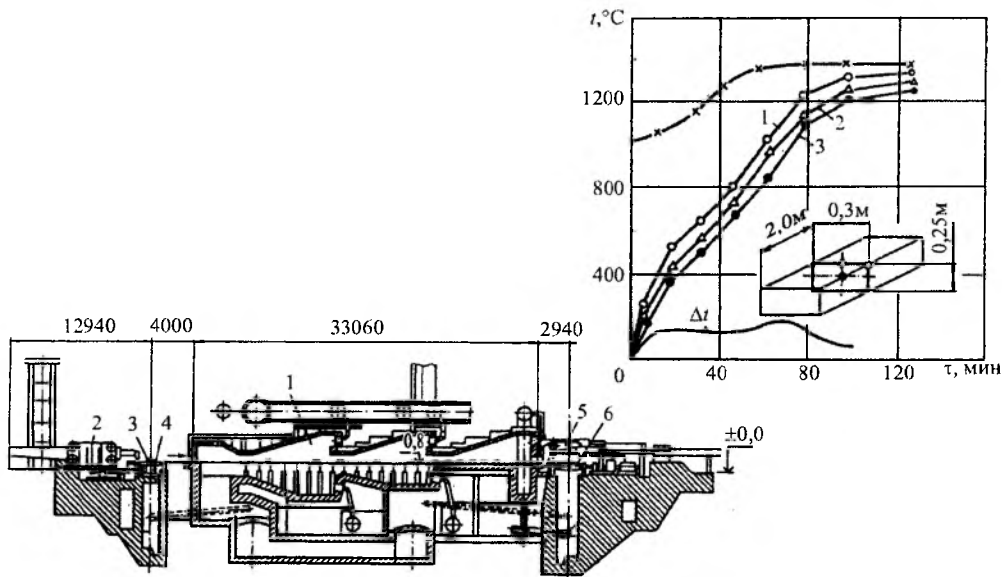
Общий вид трехзонной методической печи стана 3600 завода «Азовсталь»¹ (нагрев стали 70К, продольный разрез): 1 — печь; 2 — толкатель; 3 — загрузочный рольганг; 4 — упор; 5 — приемник слэбов²; 6 — разгрузочный рольганг
